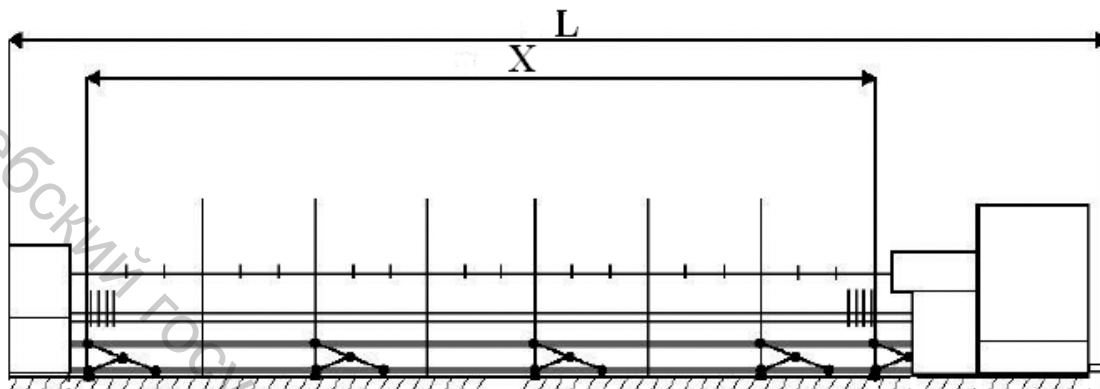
Габаритные размеры машины мод. 351 фирмы Zinser с CoWeMat 395 V сопряженной с установкой Bobbin Tray
